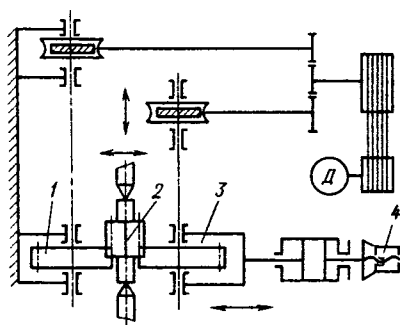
Схема процесса прикатывания шлицев на деталях типа «Вал»
